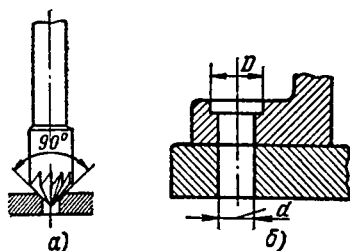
Обработка отверстия конической зенковкой (а) и отверстие, обработанное цилиндрической зенковкой (б)
